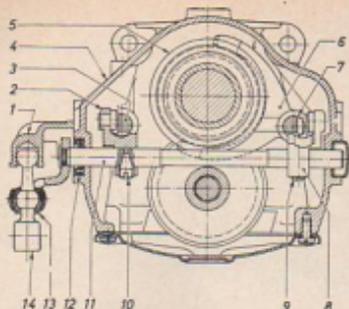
Getriebeschaltwelle in Getriebegehäuse-Einstangenschaltung
